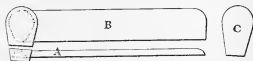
Mandrins pour la fabrication des canons Borgnet. — Vue perspective.
